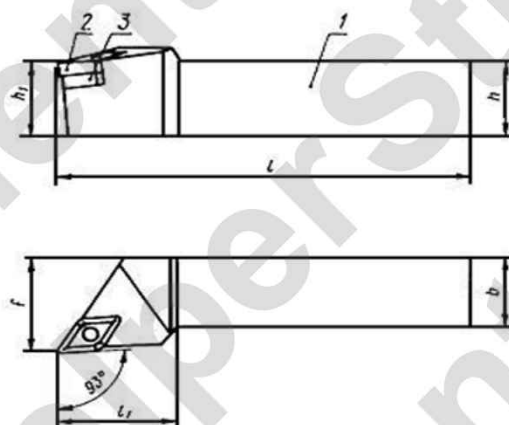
Резец токарный сборный для контурного точения с механическим креплением многогранной твердосплавной пластины ГОСТ 20872–80
